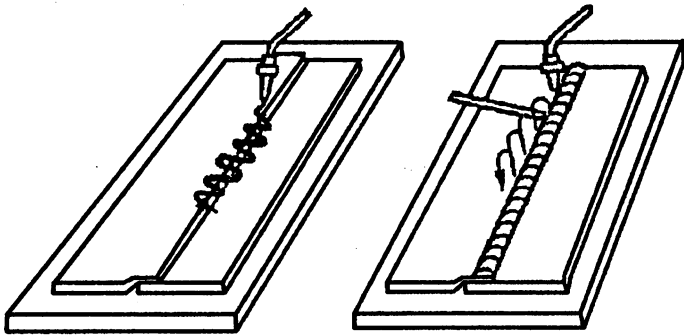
Характер руху полум'я при зварюванні окремими ванночками
